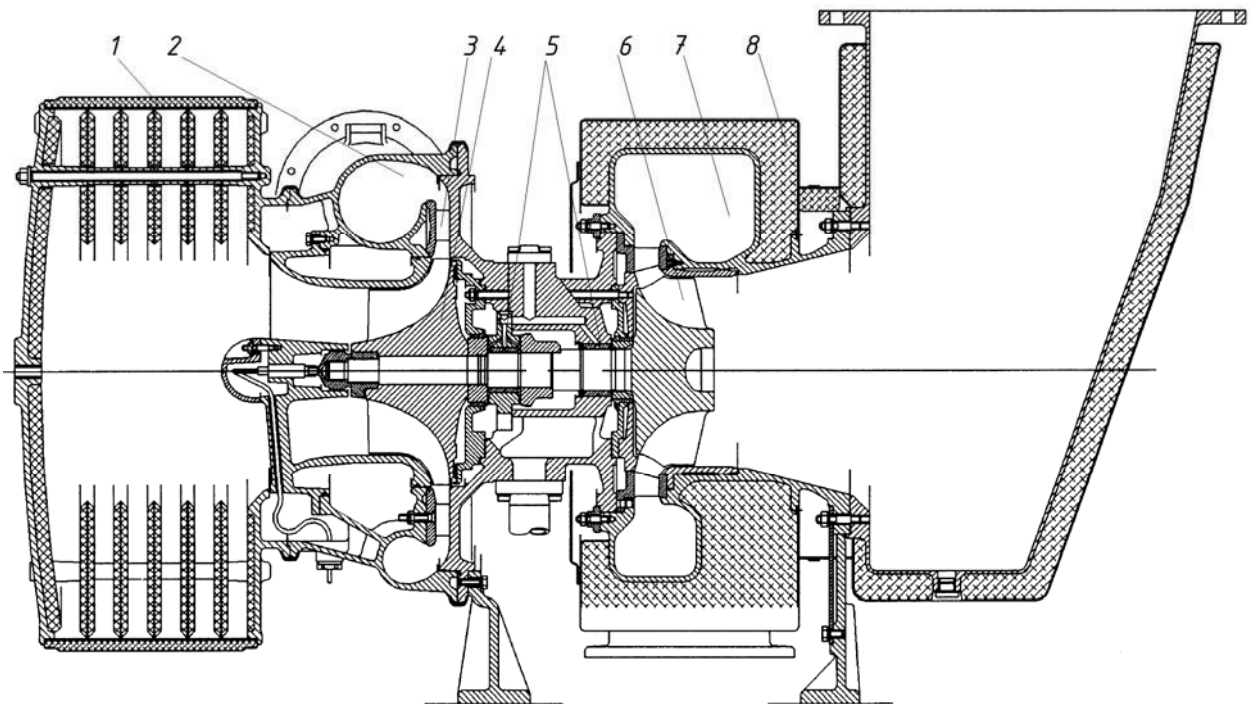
Турбокомпресор радіально-осьового типу дизеля L28/32 (NR 24R): 1 – фільтр повітря; 2 – улітка компресору; 3 – направляючий апарат компресору; 4 – колесо компресору; 5 – корпус підшипникового вузла; 6 – колесо турбіни; 7 – короб з дефлекторами для подачі газів на турбіну; 8 – теплозахисне покриття
